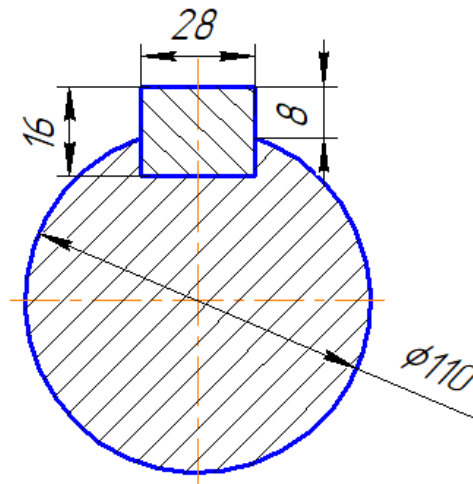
Ескіз шпонкового з'єднання вала з робочим колесом
